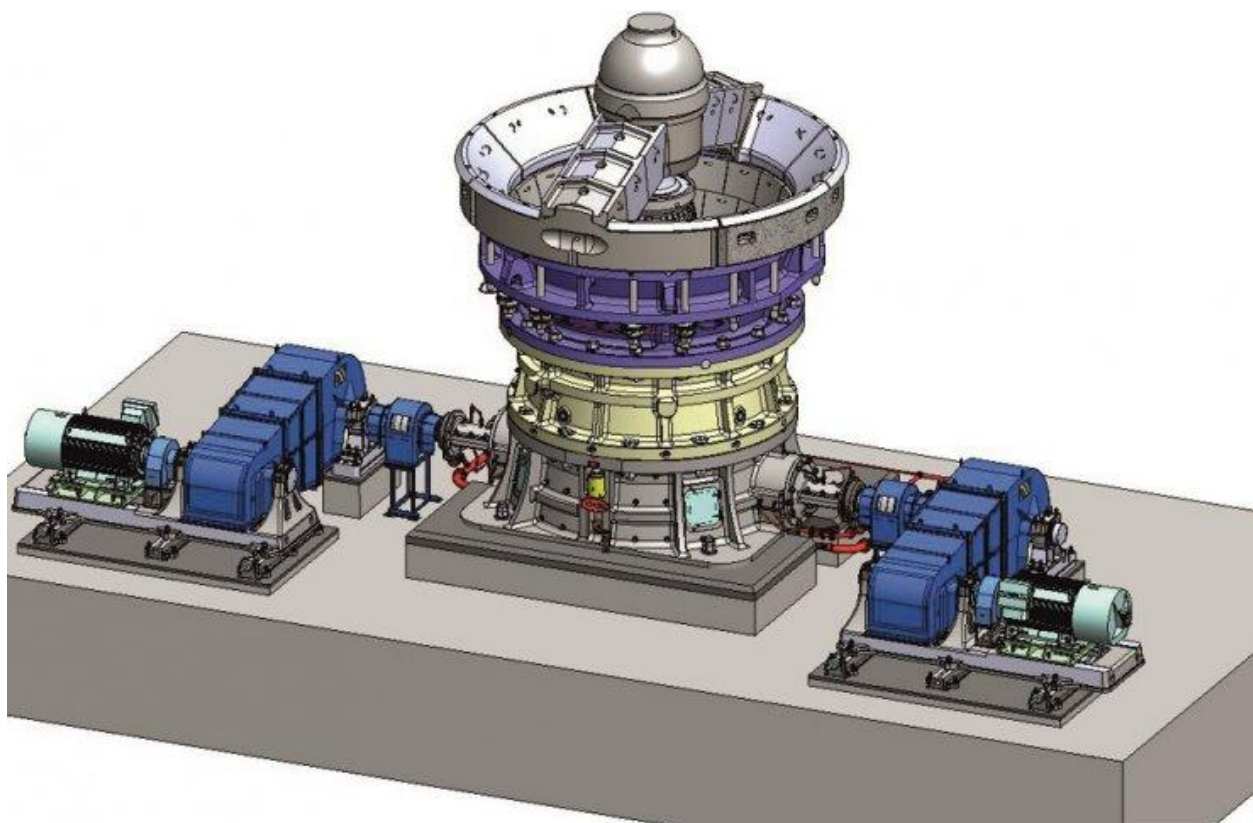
Загальний вид дробарки ККД-1500/300 (двохдвигунний варіант)
